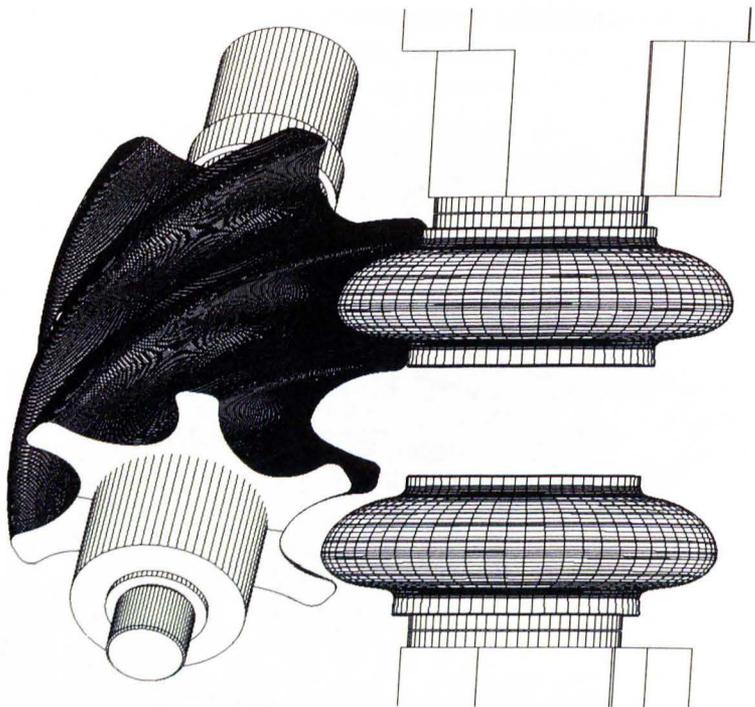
3D-Kollisionsbetrachtung Rotor / Schleifscheiben
